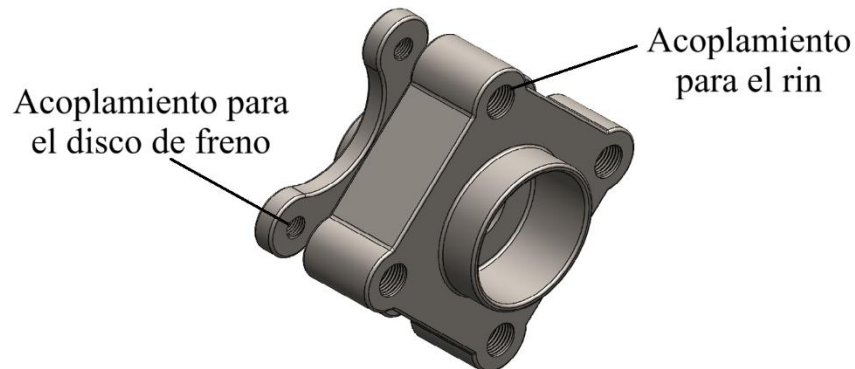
Modelo geométrico CAD 3D del cubo de la rueda en una vista isométrica.
